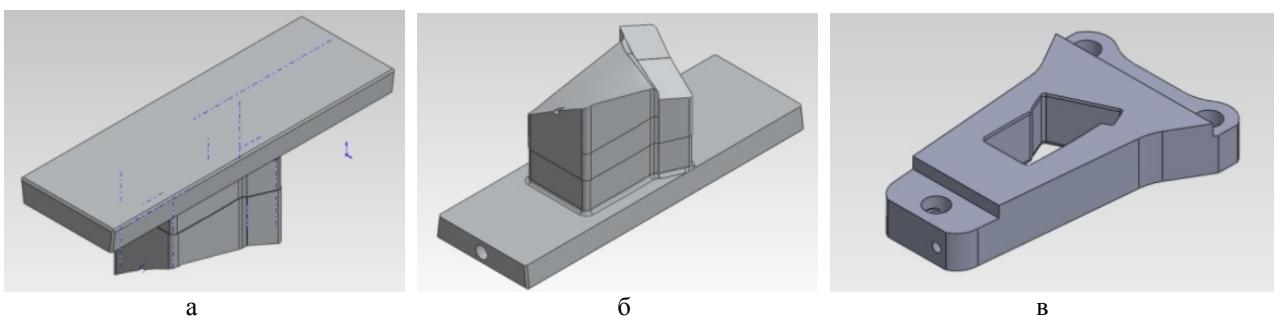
3D модель штампа для закрытой изотермической штамповки:
